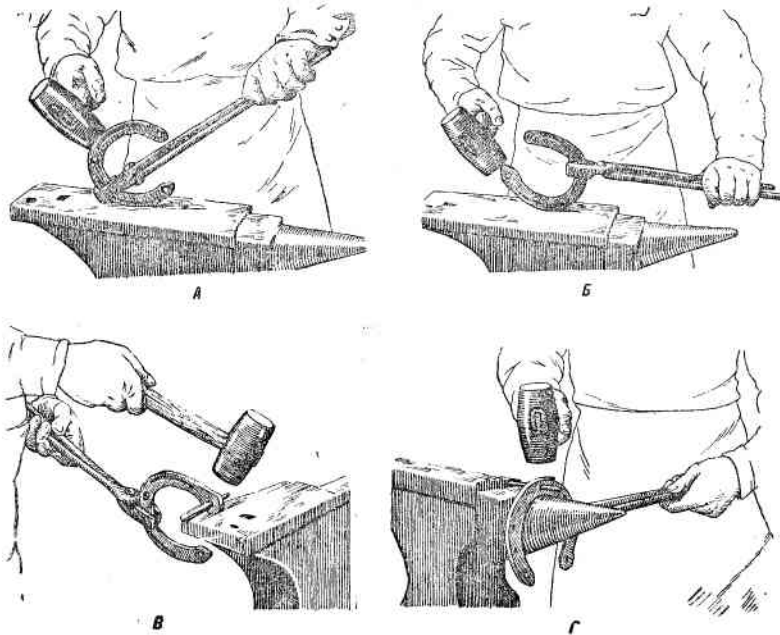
Высадка и оправка шиповых отверстий в подкове:
